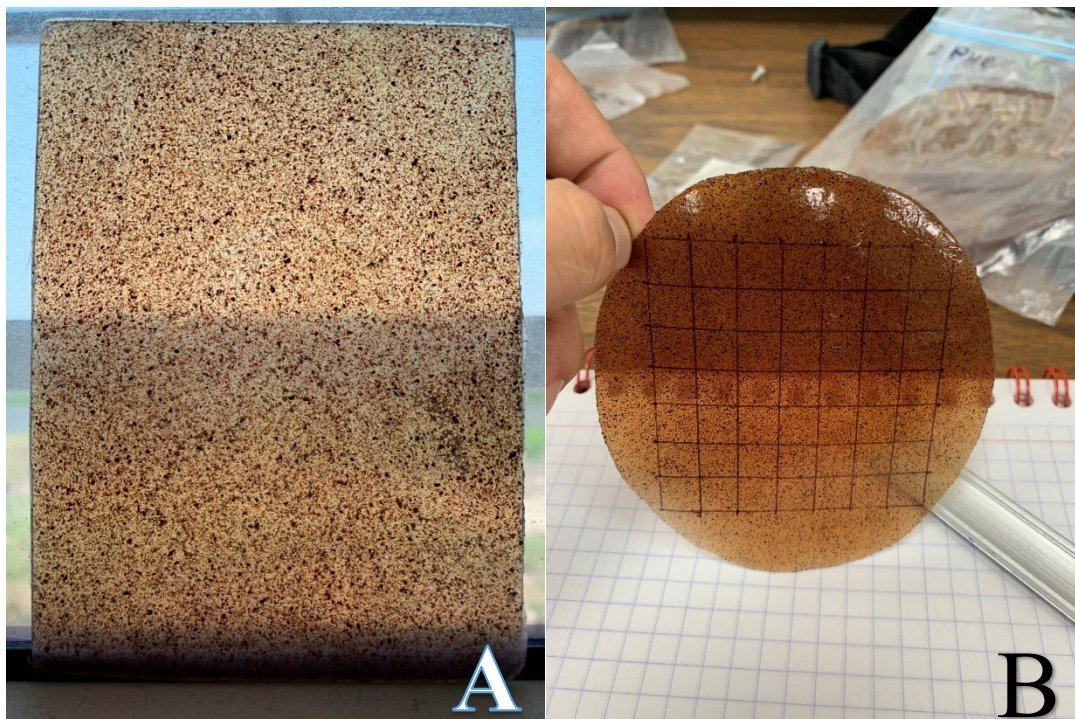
Laminas obtenidas de la técnica moldeo por compresión. A) con molde de 10 cm x 15 cm x 0.26 cm., B) sin molde utilizando dos placas metálicas con acetato.
